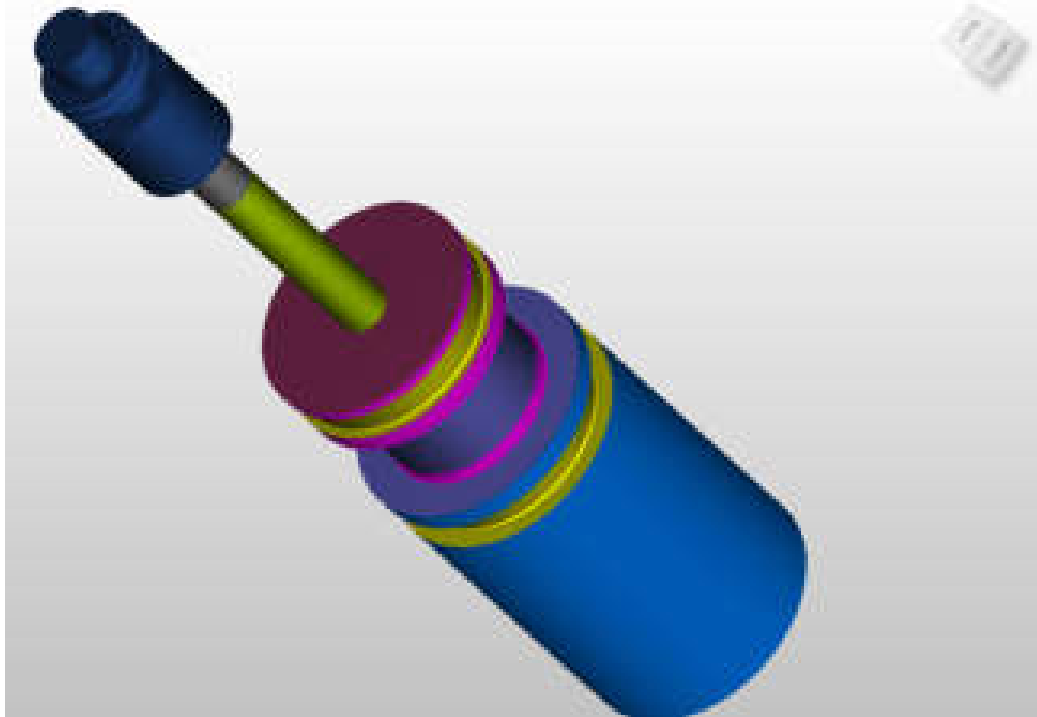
Операція фрезерна з ЧПУ: контурне фрезерування
